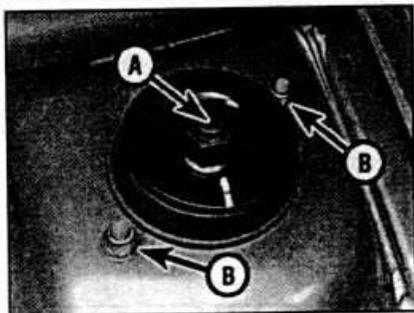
Расположение защитной головки (А) центральной гайки стойки и гаек (В) крепления передней стойки к кузову.
